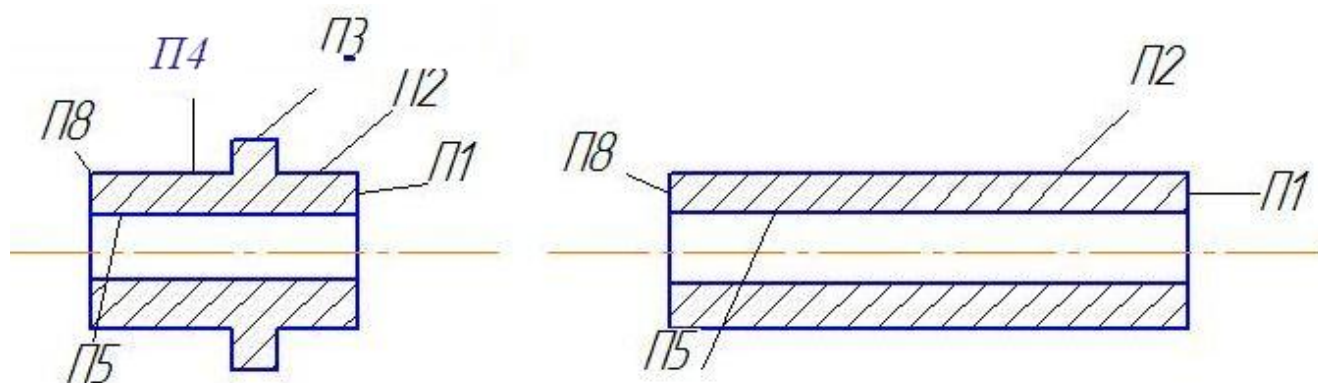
Детали для разработки индивидуальных техпроцессов
